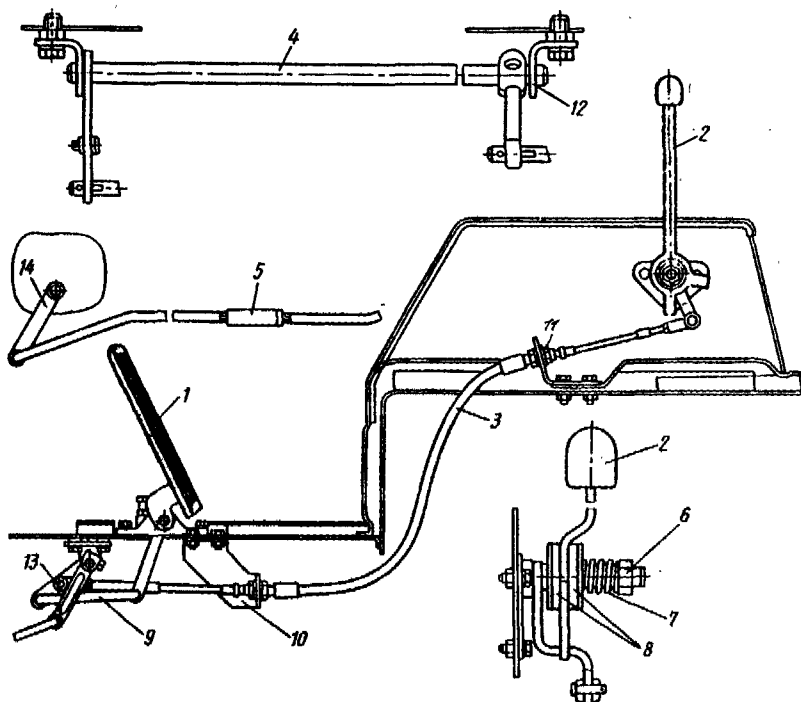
Привод управления подачей топлива (МТЗ-100, МТЗ-102): 1 – педаль; 2 – рукоятка ручного управления; 3 – трос; 4 – поперечный валик; 5 – тяга с регулировочной муфтой; 6 – гайка; 7 – пружина; 8 – фрикционные диски; 9 – промежуточная тяга; 10 – кронштейн; 11 – задний кронштейн; 12 – кронштейны поперечного валика; 13 – регулировочные вилки троса; 14 – рычаг топливного насоса
